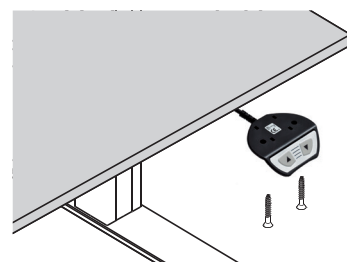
Handschalter LegaDrive Basic am Beispieltisch anbringen
